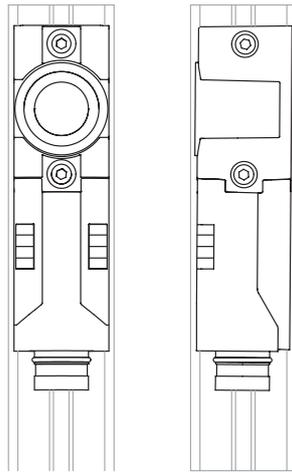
Montageausrichtungen frontseitige und seitliche Befestigung
